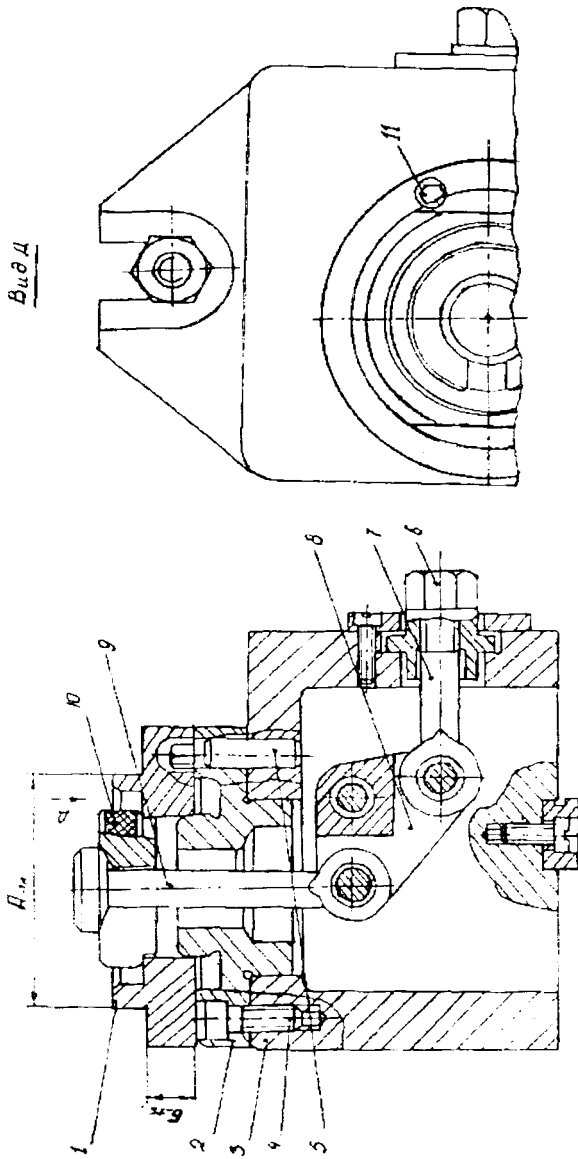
Стенда пьное фрезерное приспособление с ручным управлением
